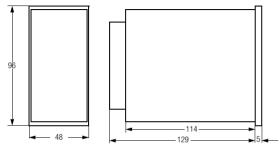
, Gehäuseabmessungen und Schalttafelausschnitt
